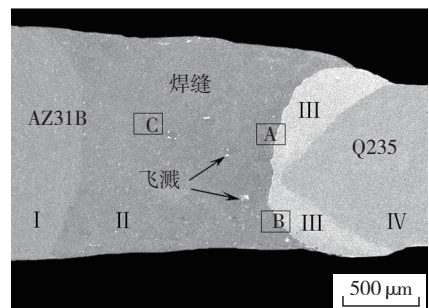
镁/钢对接结构激光-电弧复合焊接接头横截面
